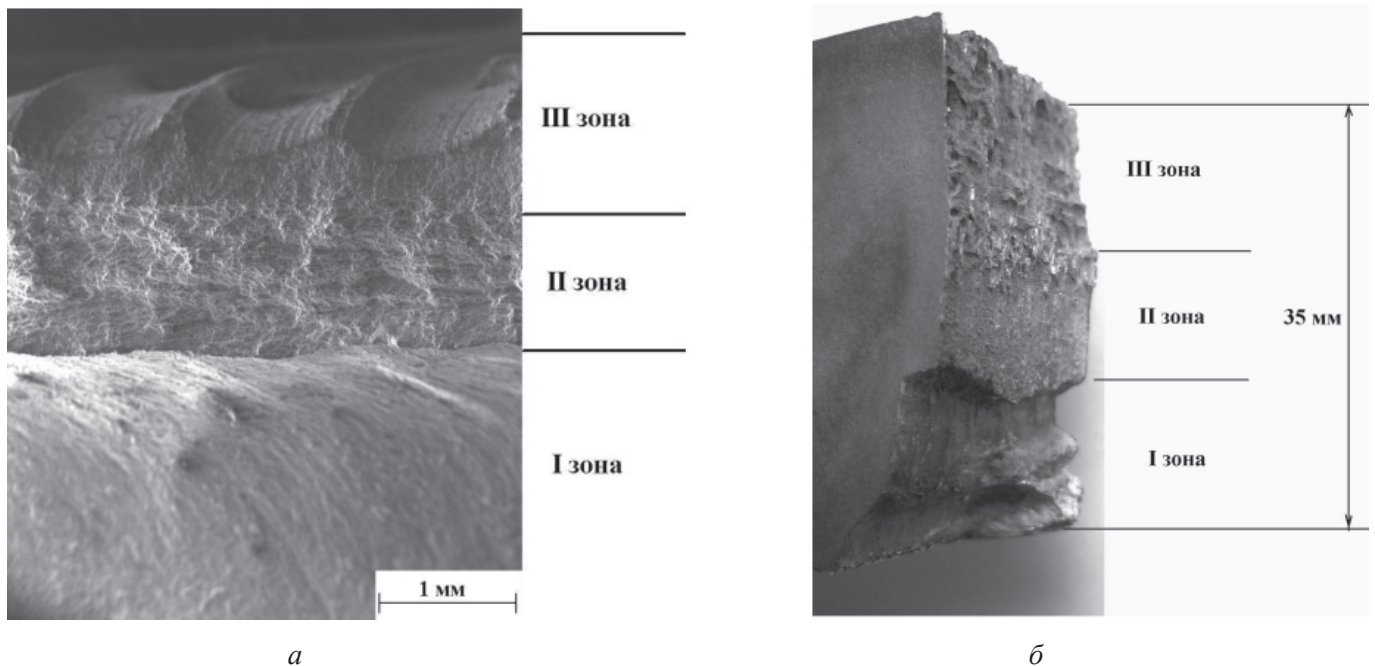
Топография поверхности разрушения сварных соединений, полученных сваркой трением с перемешиванием:
